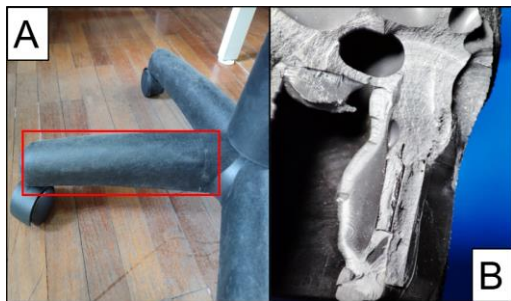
(A) Soporte en donde ocurrió la falla progresiva. (B) Superficie de fracturada del componente polimérico (vista macro).
